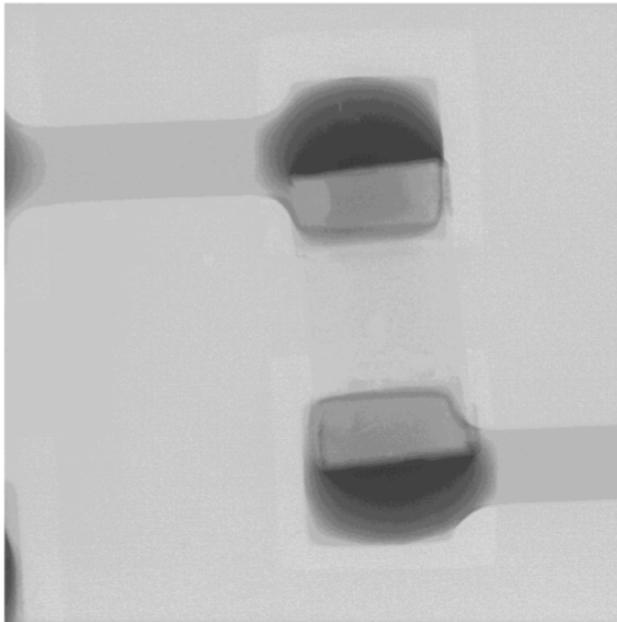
Se observa una soldadura sin defectos en el componente electrónico.
